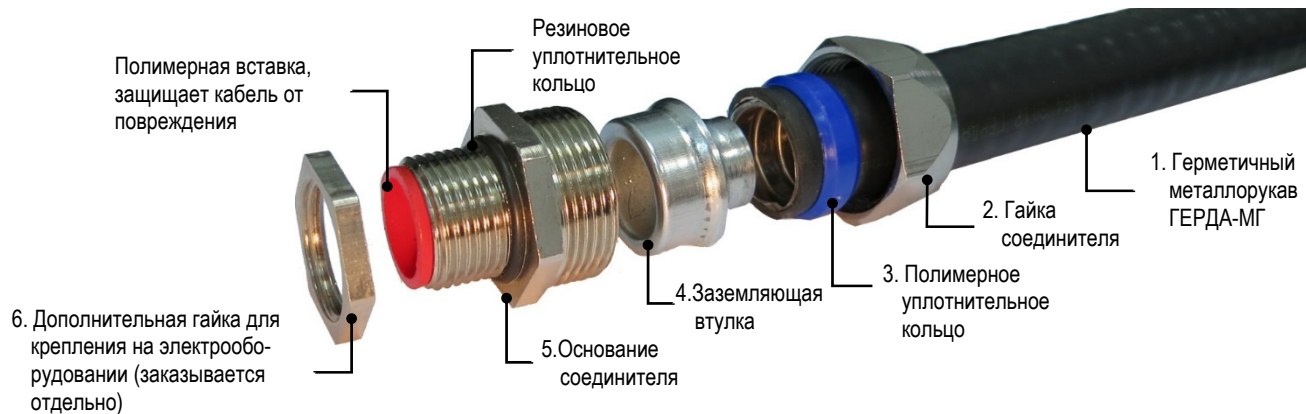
Устройство соединителя GERDA-SГ с наружной резьбой «Н». Соединитель с внутренней резьбой «В» отличается резьбой основания (5).
